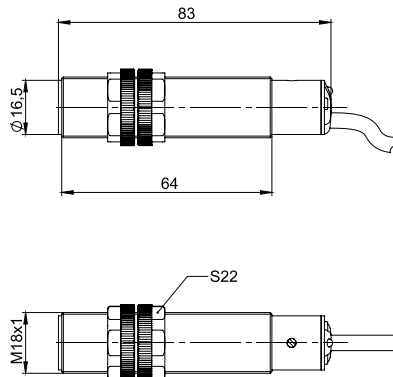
Габаритные и установочные размеры датчиков CAP18 с кабельным выводом
